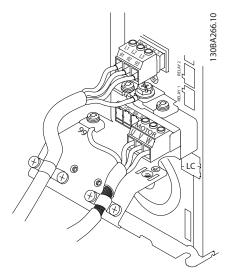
Проводка двигателя, питания и заземления для типоразмера A
